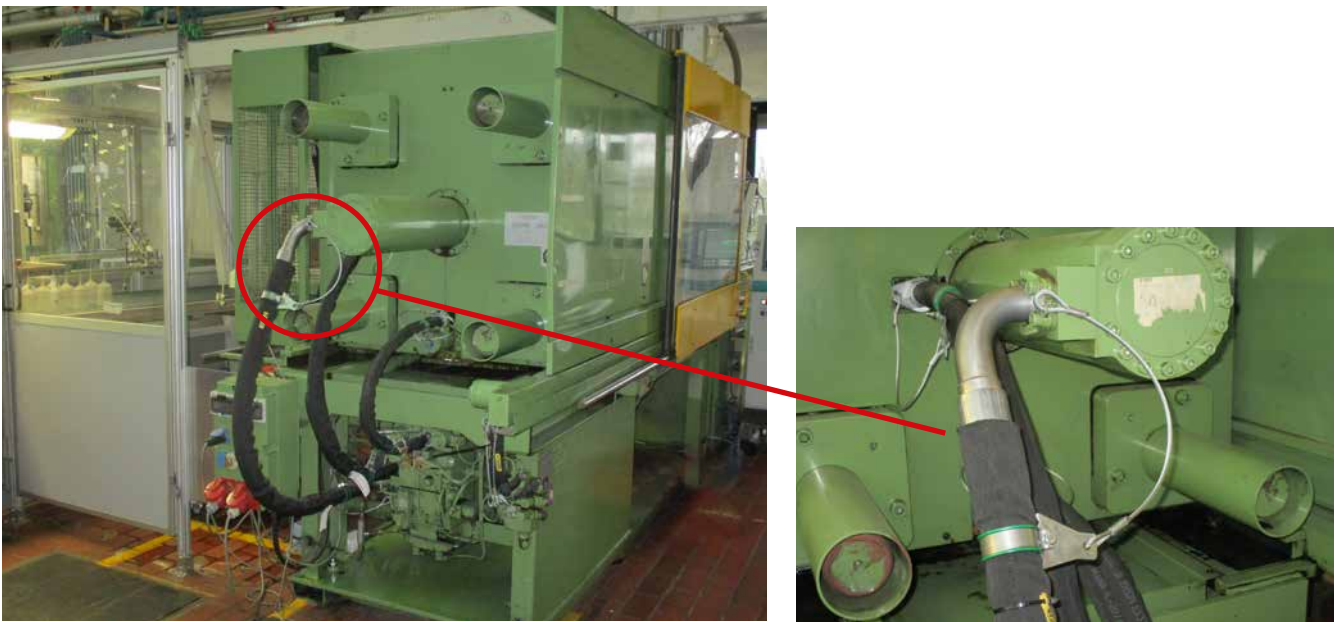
a + b Best practice für Hydraulikanschlüsse mit Fangsicherung an einer Spritzgießmaschine
